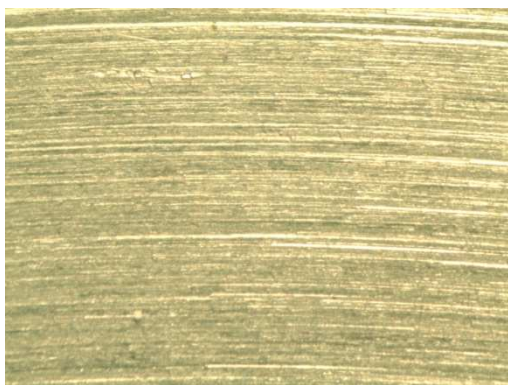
a 52 Obrobena plocha vzorku s použitím vody
